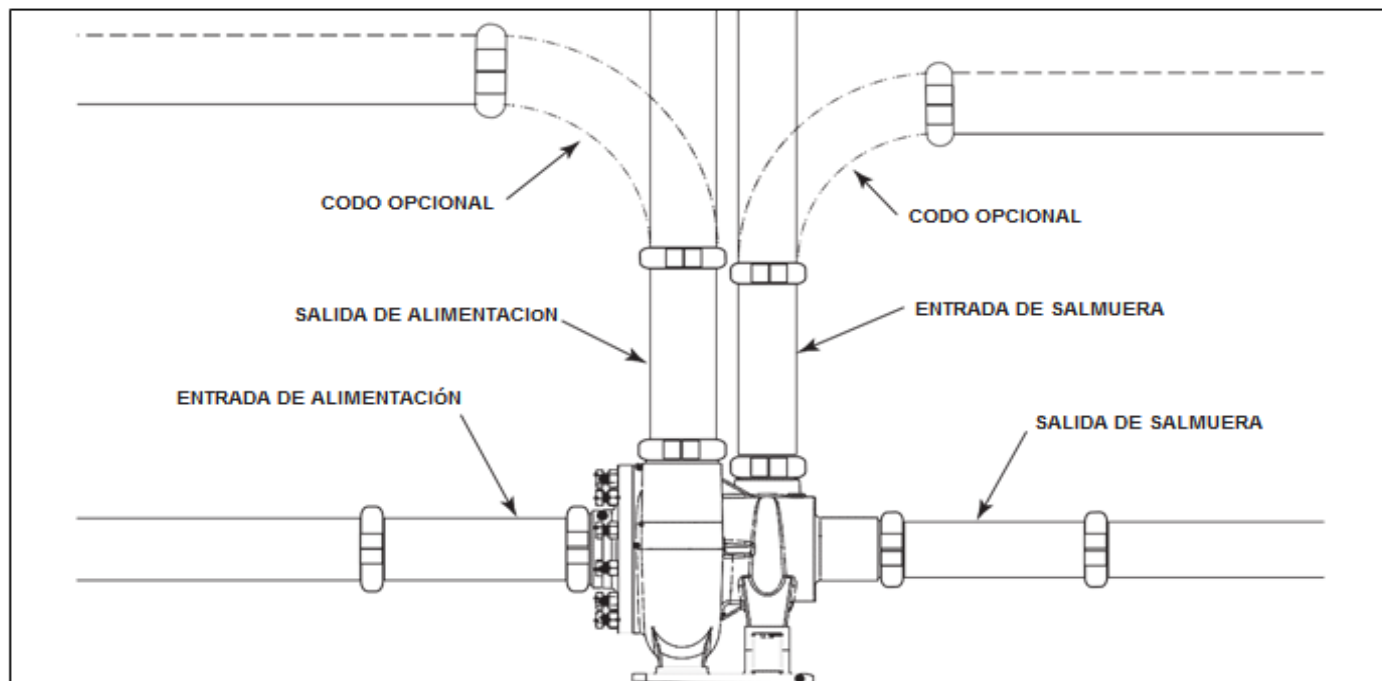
Secciones desmontables para el servicio del aumentador de presión
